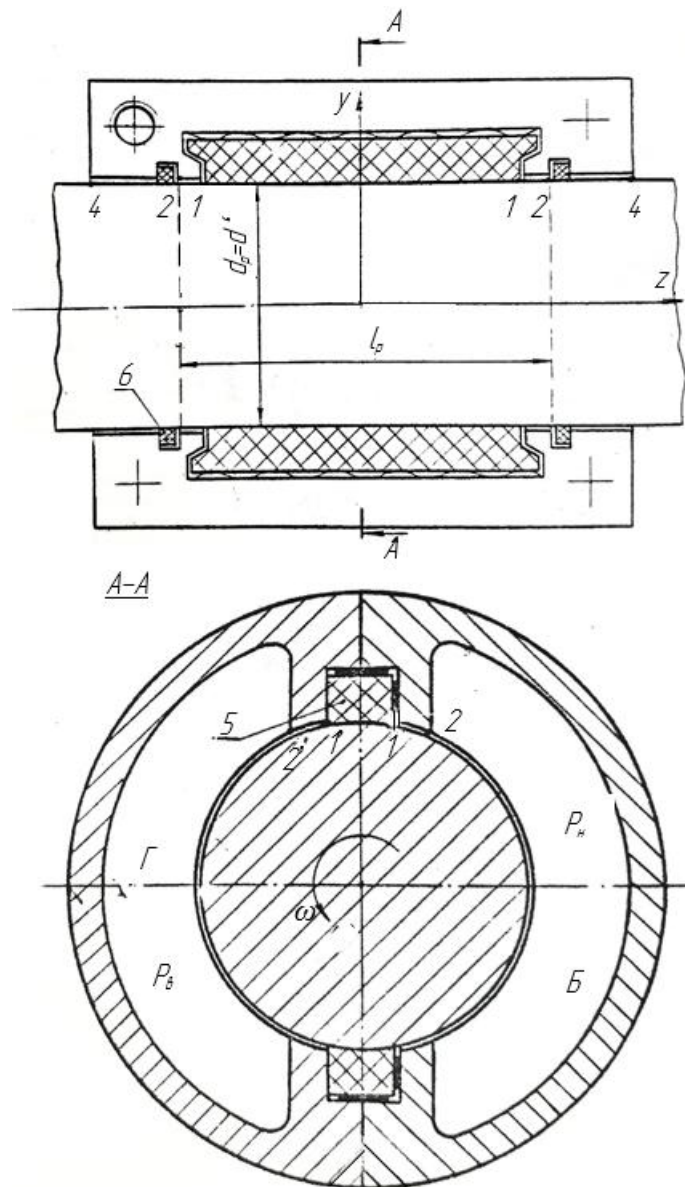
Конструкция разгрузочной камеры винтового компрессора
